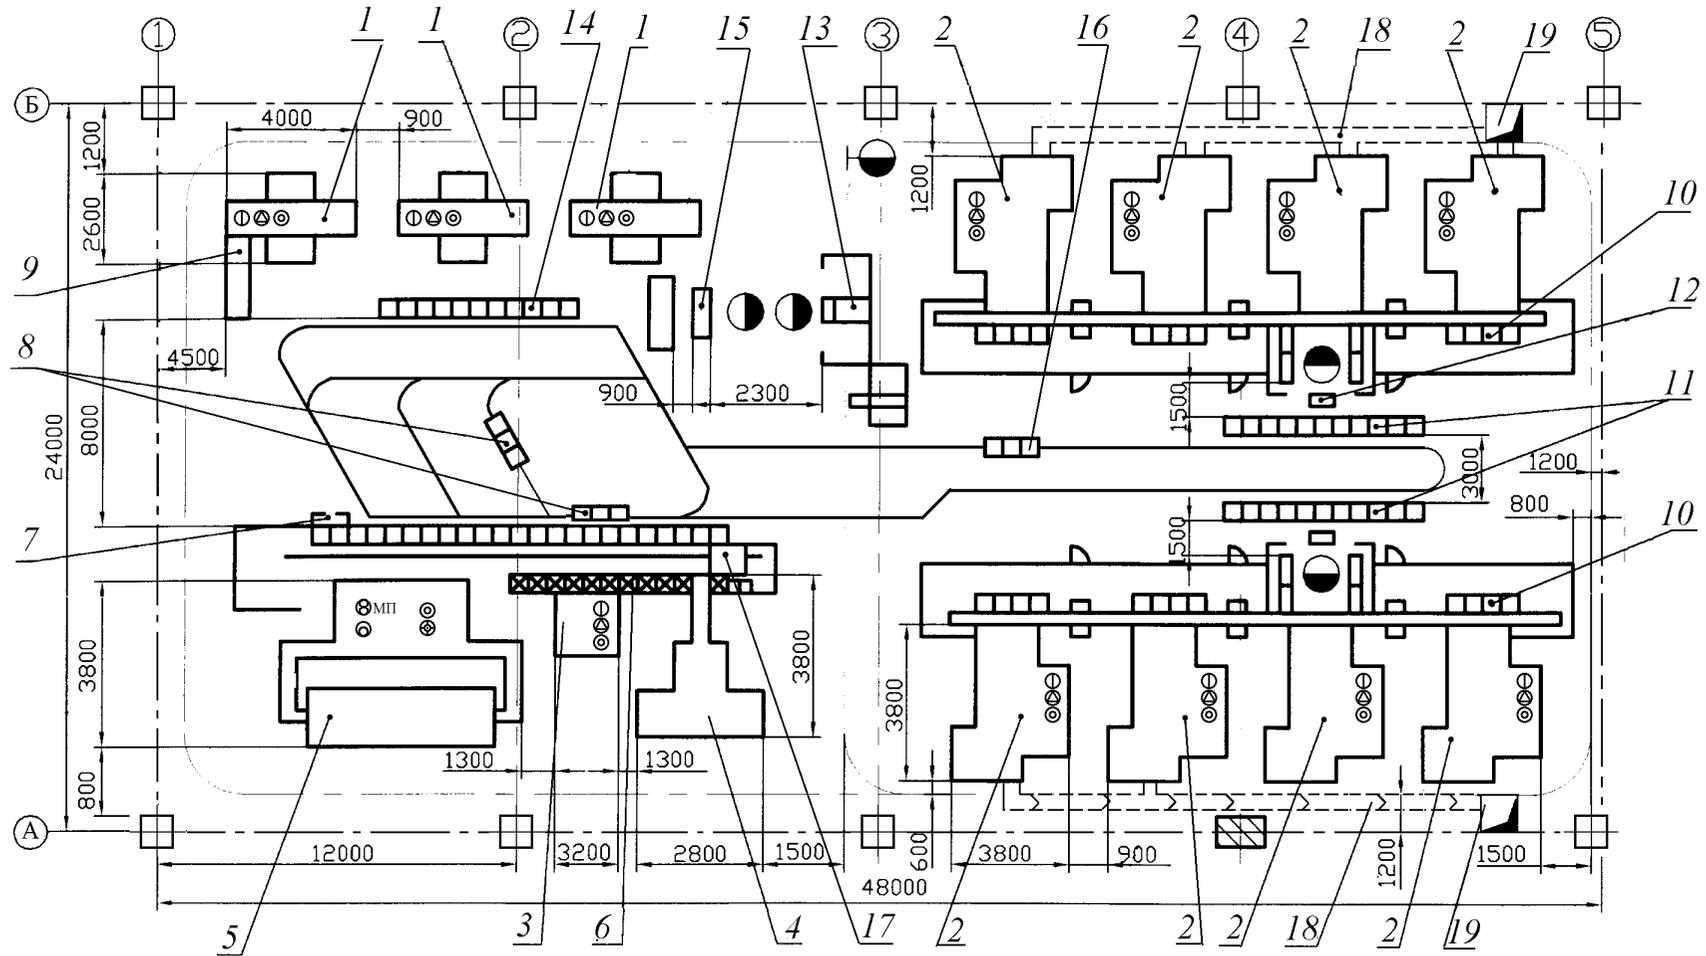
П14. ГПУ для обработки корпусных деталей:
